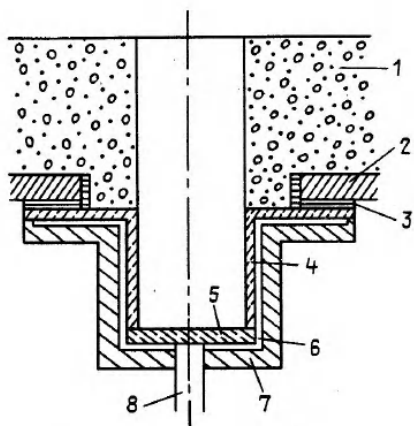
Схема подового электрода конструкции Slesim: 1 - огнеупорная набивка; 2 - кожух; 3 - изоляция; 4 - юбка стержня токоподвода; 5 - основание стержня токоподвода; 6 - циркулирующая вода охлаждения; 7 - защитная оболочка; 8 - токоподвод
